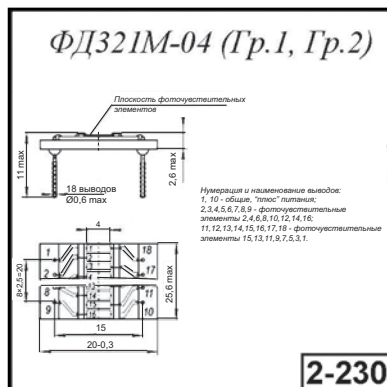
Внешний вид, габаритные размеры кремниевых фотодиодов
